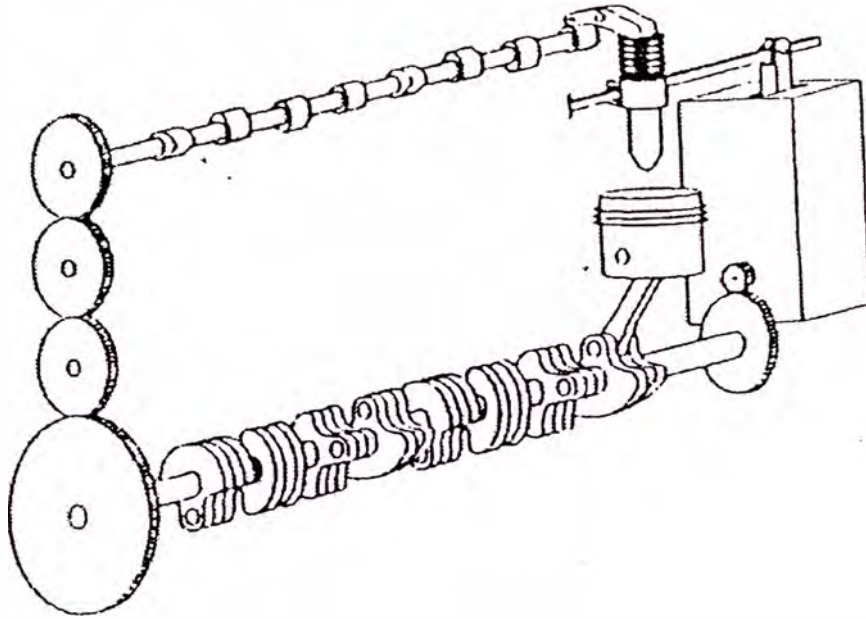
3. e Sistema mecánico de inyección de combustible
